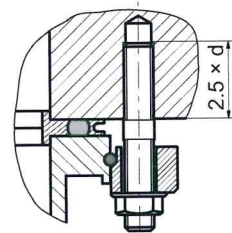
Flanschverbindung ISO-K zu ISO-F, Stiftschraube und Gewindebohrung
